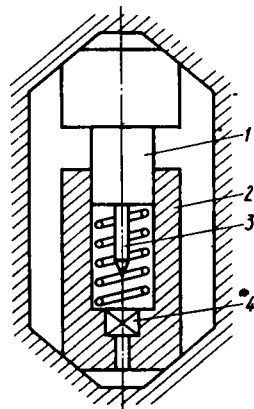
Конструктивная схема всюдубойного механизма взрывателя
